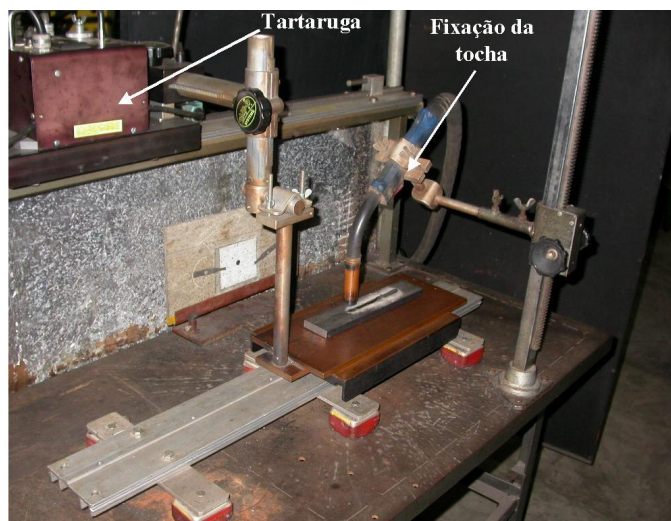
Mesa de soldagem mecanizada com sistema de deslocamento do corpo de prova
